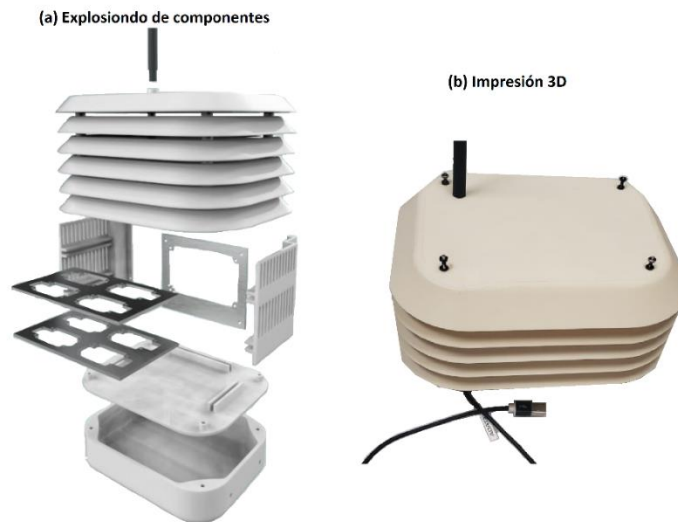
Prototipo de nodo sensor versión 2 [42], (a) Explosión de componentes, (b) Impresión 3D.
